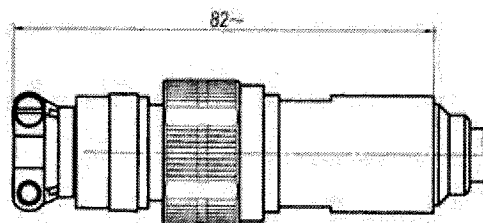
Кресленик зовнішньої частини ТХА-1690, ТХК-1690 з головкою типу БАУИ.4087234.025 СБ
